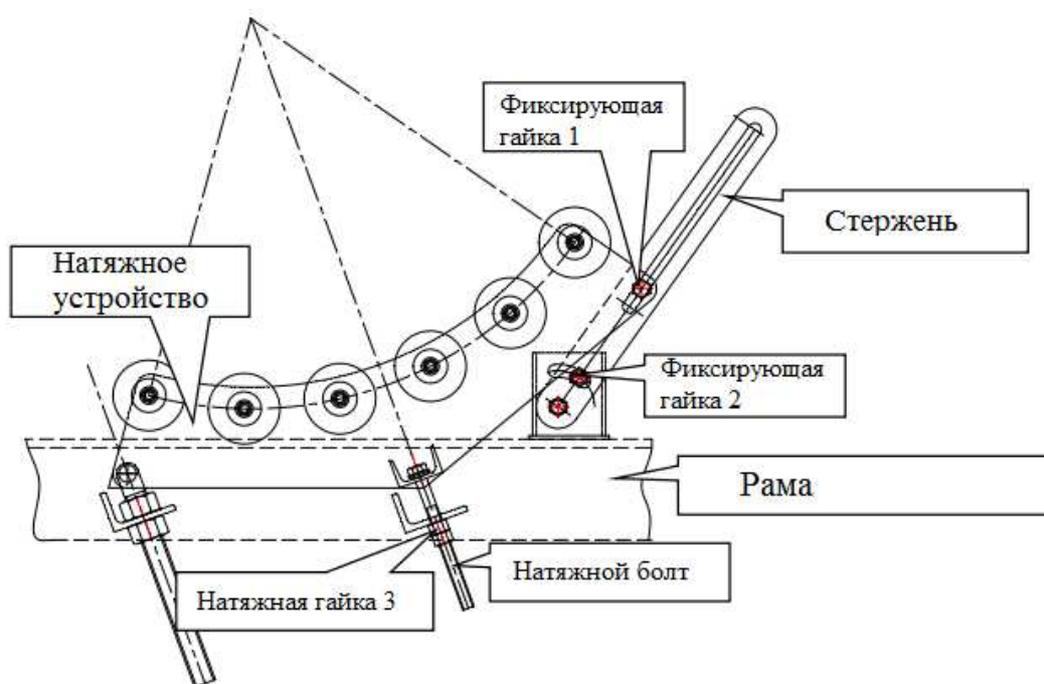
Регулировка устройства натяжения поручня.
